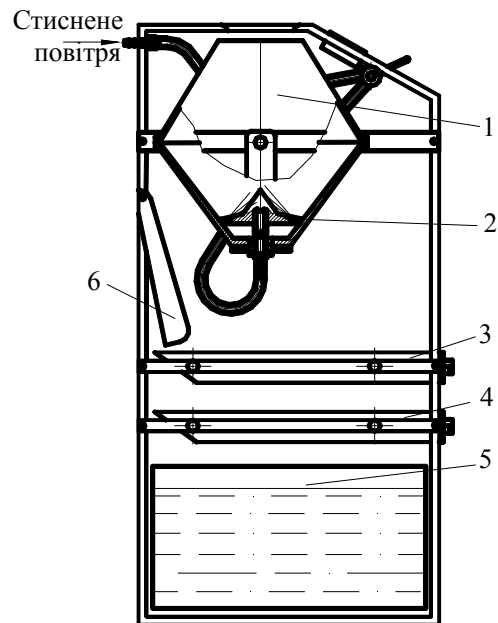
Схема лабораторної струминно-абразивної установки з об'ємом робочої камери 30 л: 1 – робоча камера; 2 – сопловий апарат (завихрювач); 3 – решето для деталей; 4 – решето для абразивного зерна; 5 – бак-відстійник; 6 – ринва для суспензії
